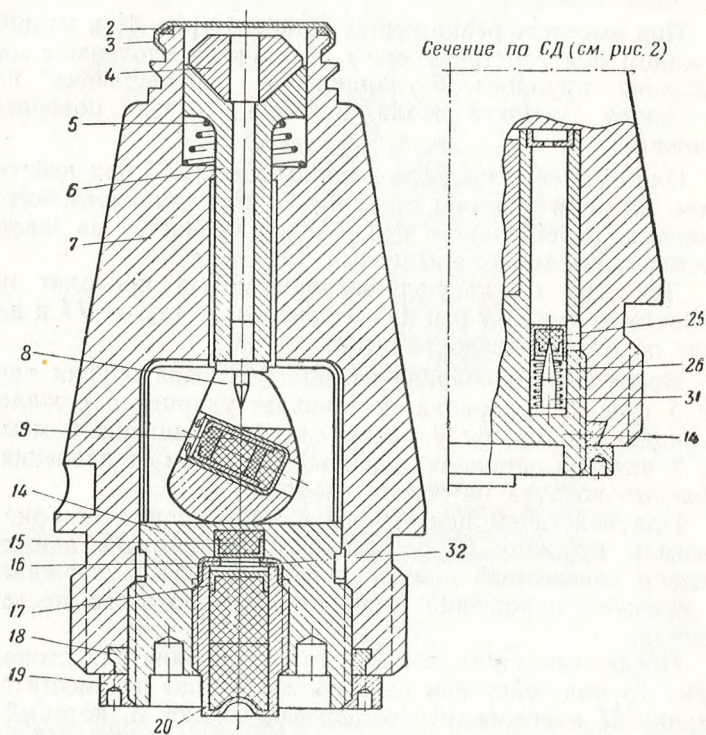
Положение деталей взрывателя при выстреле: 2— прокладка под мембрану; 3— мембрана; 4— реакционная шайба ударника; 5— пружина ударника; 6— ударник с жалом; 7— корпус; 8— поворотный движок; 9— капсюль-детонатор; 14— втулка поворотного движка; 15— передаточный заряд; 16— крышка; 17— чашечка детонатора; 18— кольцо; 19— гайка; 20— стакан детонатора снаряженный; 25— капсюль-воспламенитель; 26— пружина; 31— жало; 32— прокладка
